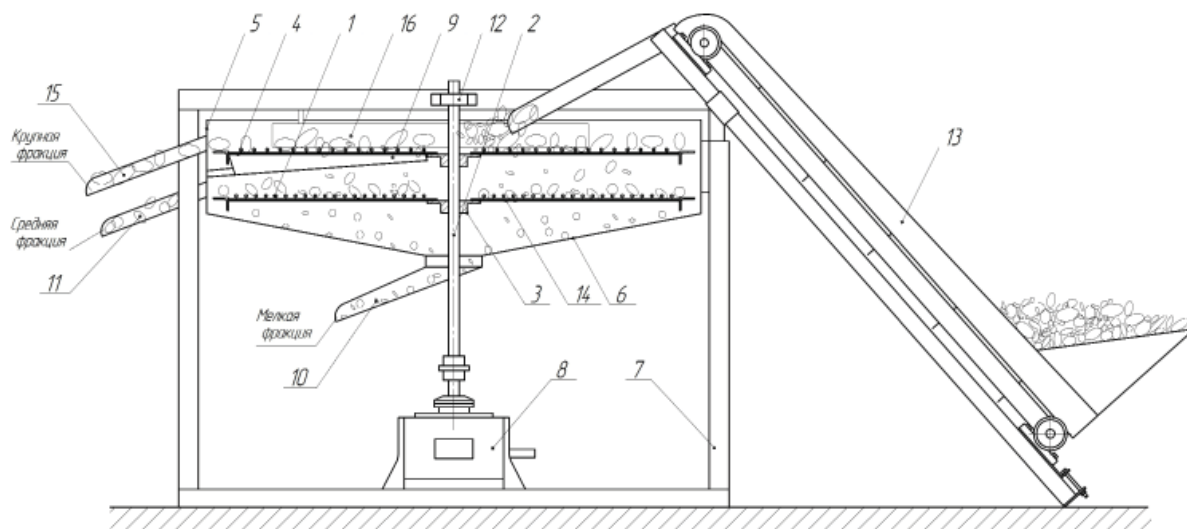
Схема работы чашечно-дисковой сортировки: 1 – второе решето; 2 – вал; 3 – ступица; 4 – первое решето; 5 – обод кожуха; 6 – приемник; 7 – рама; 8 – редуктор; 9 – подъемная планка; 10 – выгрузной лоток мелкой фракции; 11 – выгрузной лоток средней фракции; 12 – подшипник; 13 – питающий транспортер; 14 – спица; 15 – выгрузной лоток крупной фракции; 16 – сектор-обод
